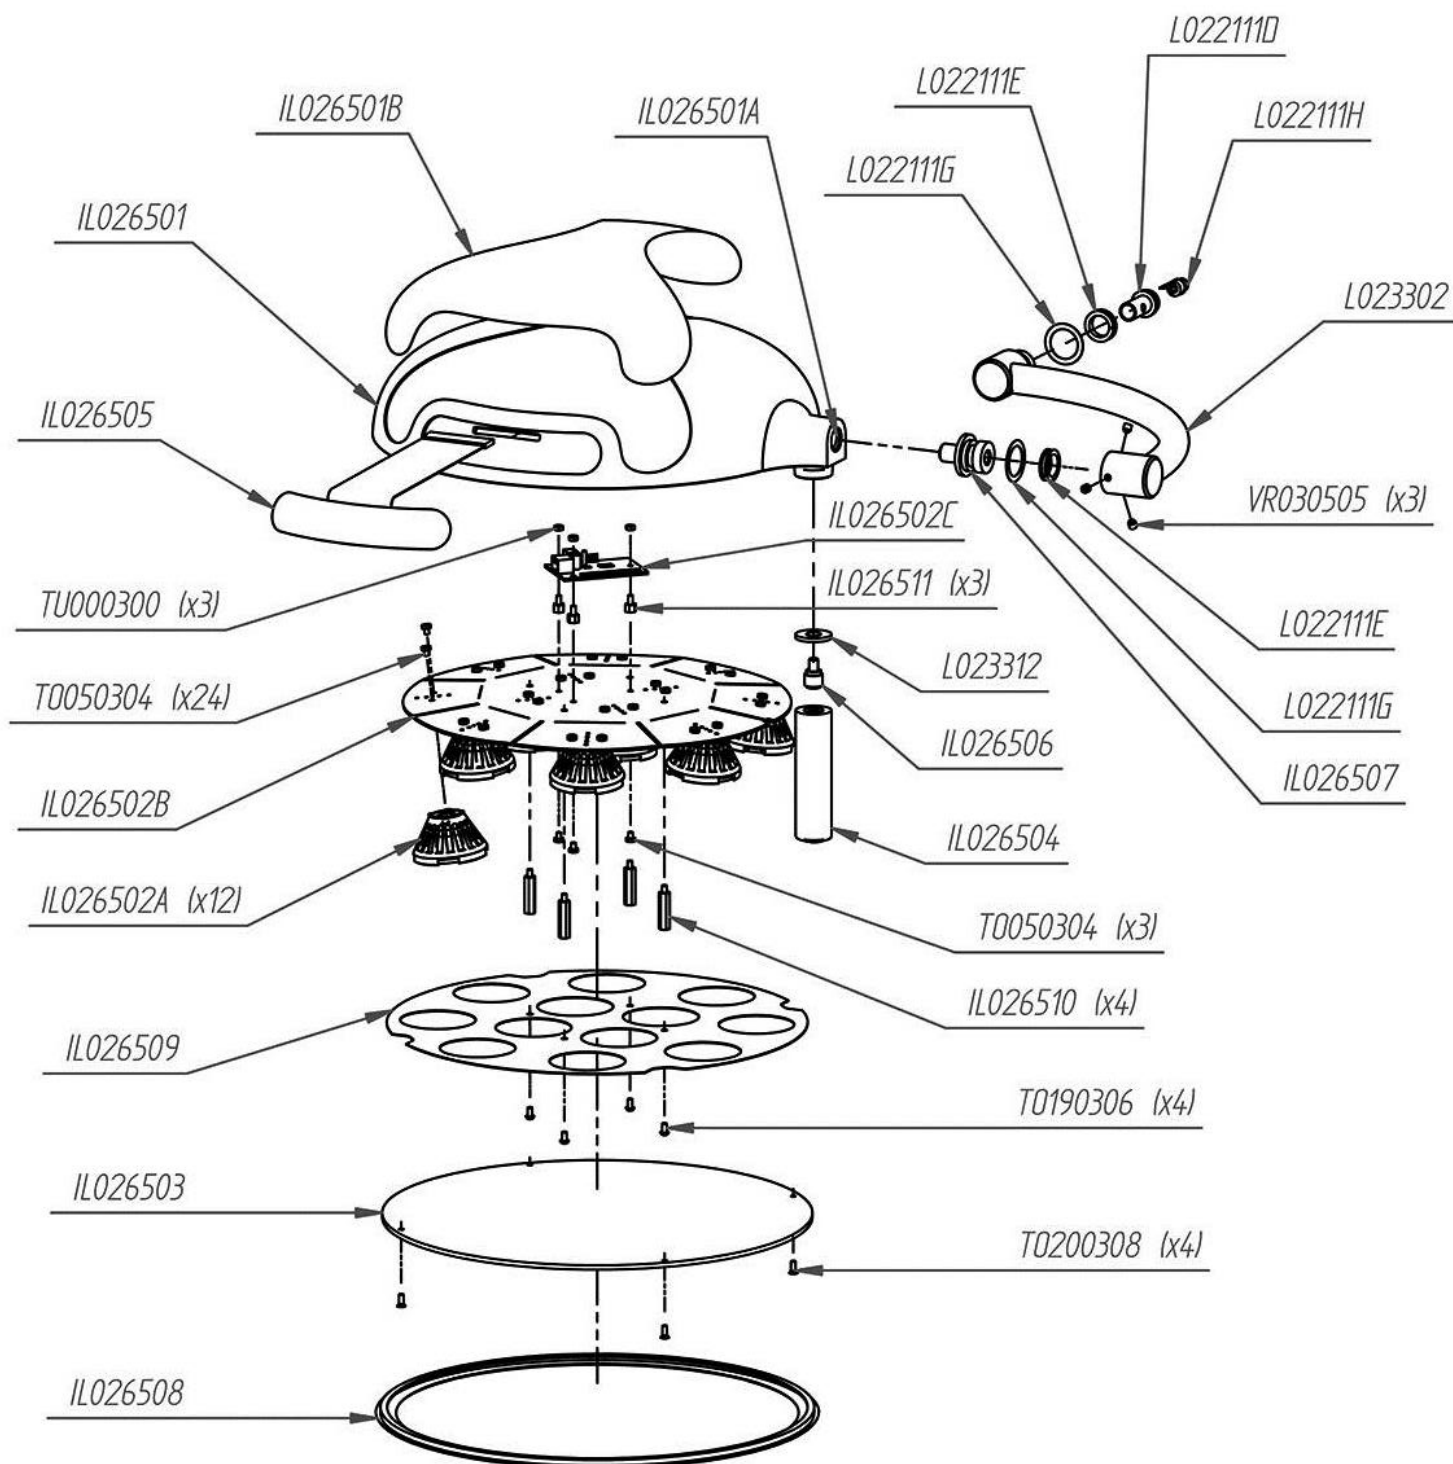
Despiece de la cúpula / Exploded view of the headlight
